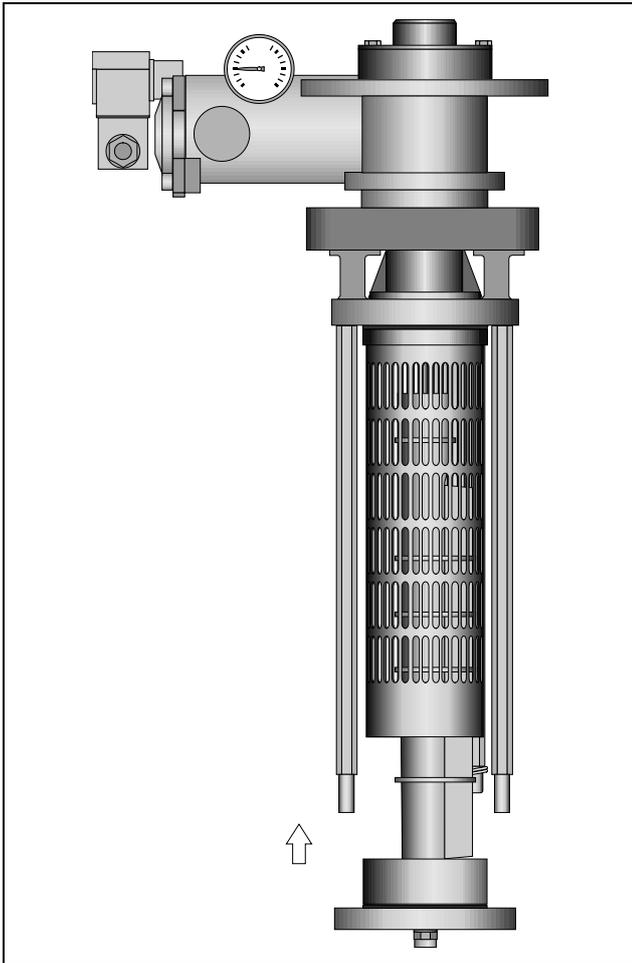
Vormontierte Baugruppe in Filterelement einbauen
